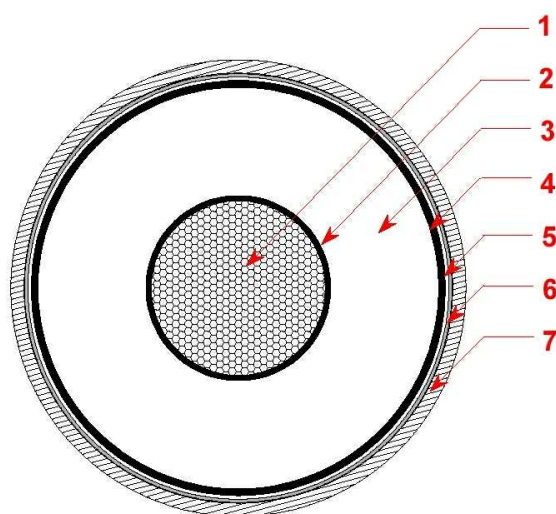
Disegno tipico (non in scala) del cavo di potenza con conduttore metallico ed isolamento estruso
